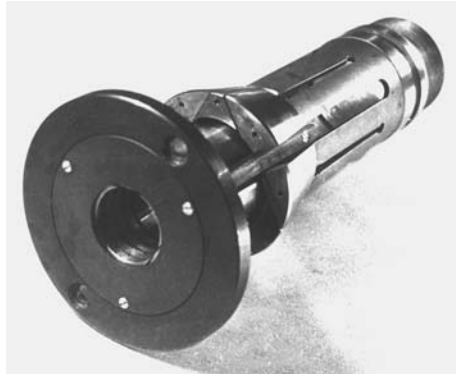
Широкодіапазонний цанговий патрон підвищеної точності до багатшпindelного токарного автомата
